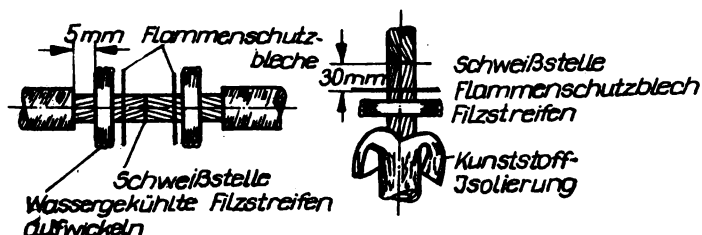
Schweißanordnung für ein Kunststoffkabel
